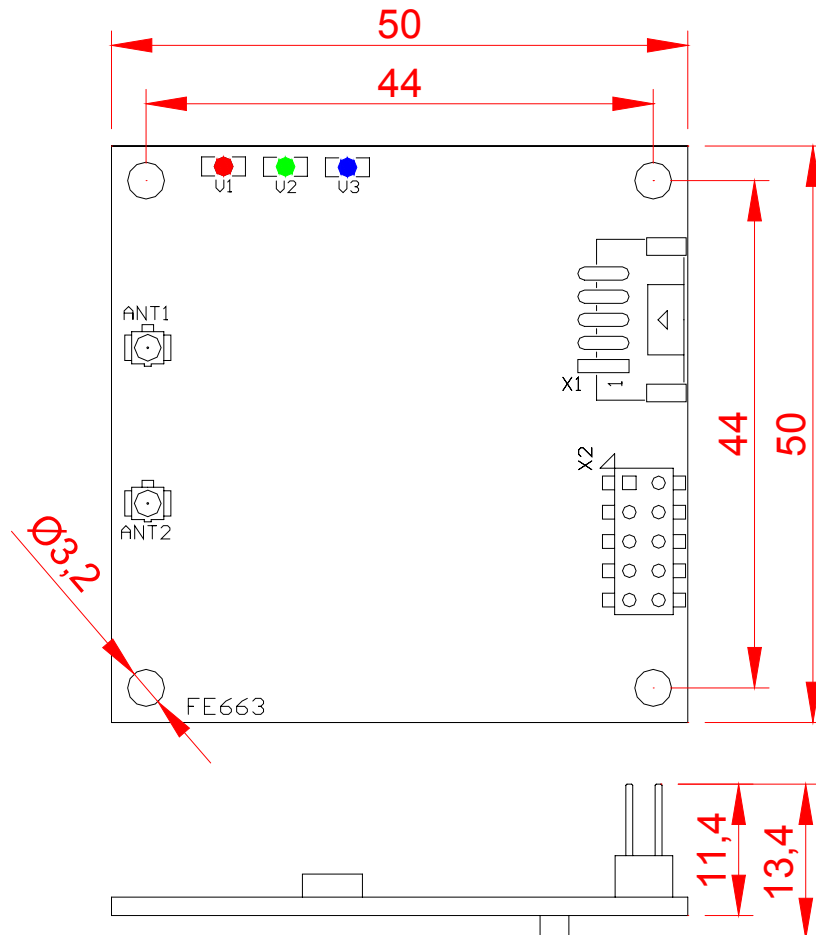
Maßzeichnung des Readermoduls ID ISC.MU02.02 in mm
